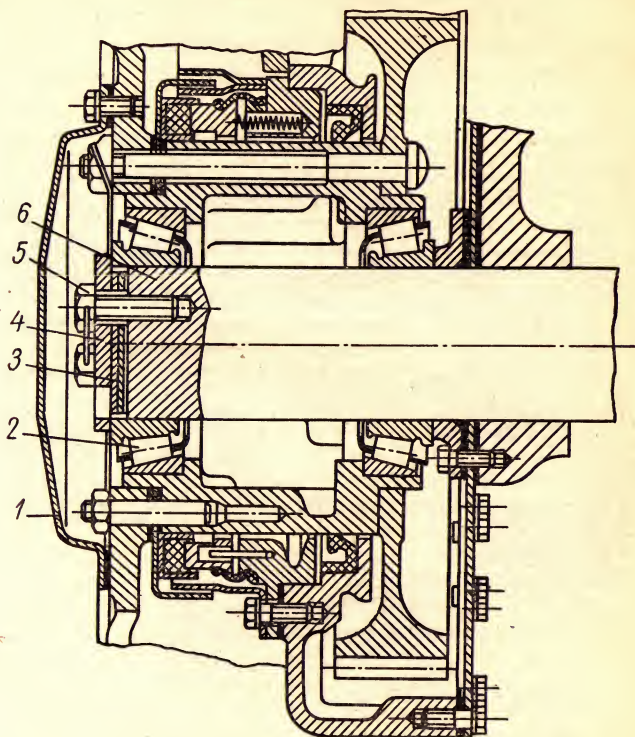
Ступица ведомой шестерни конечной передачи трактора Т-74:
